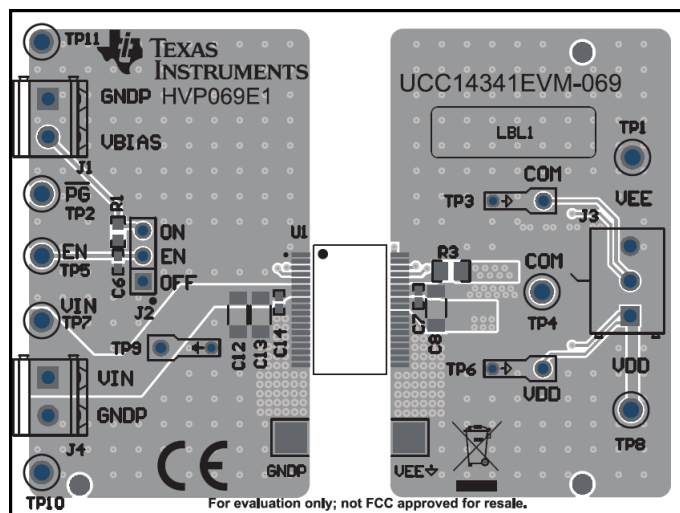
UCC14340-Q1EVM , PCB 顶层 , 组装
